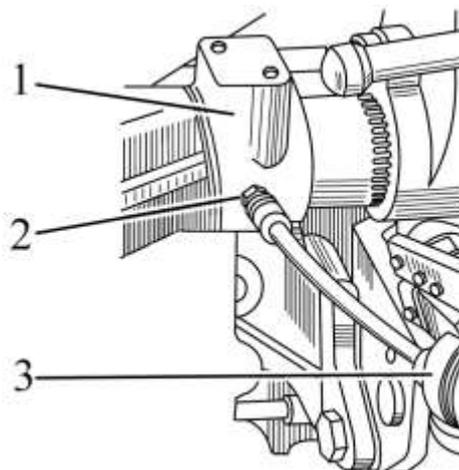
Смазка втулок поворотного вала ЗНУ
